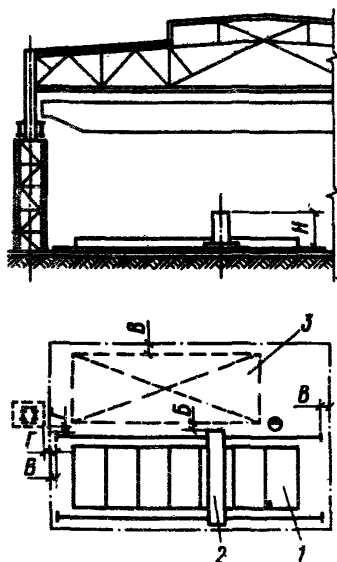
Размещение сборочного стеллажа с передвижным прижимом
